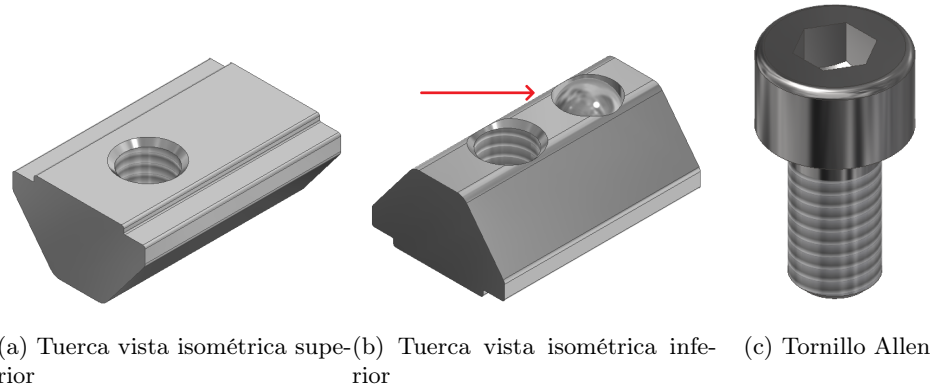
Tuerca y tornillo que se utilizará para el ensamblaje de diversos componentes.
